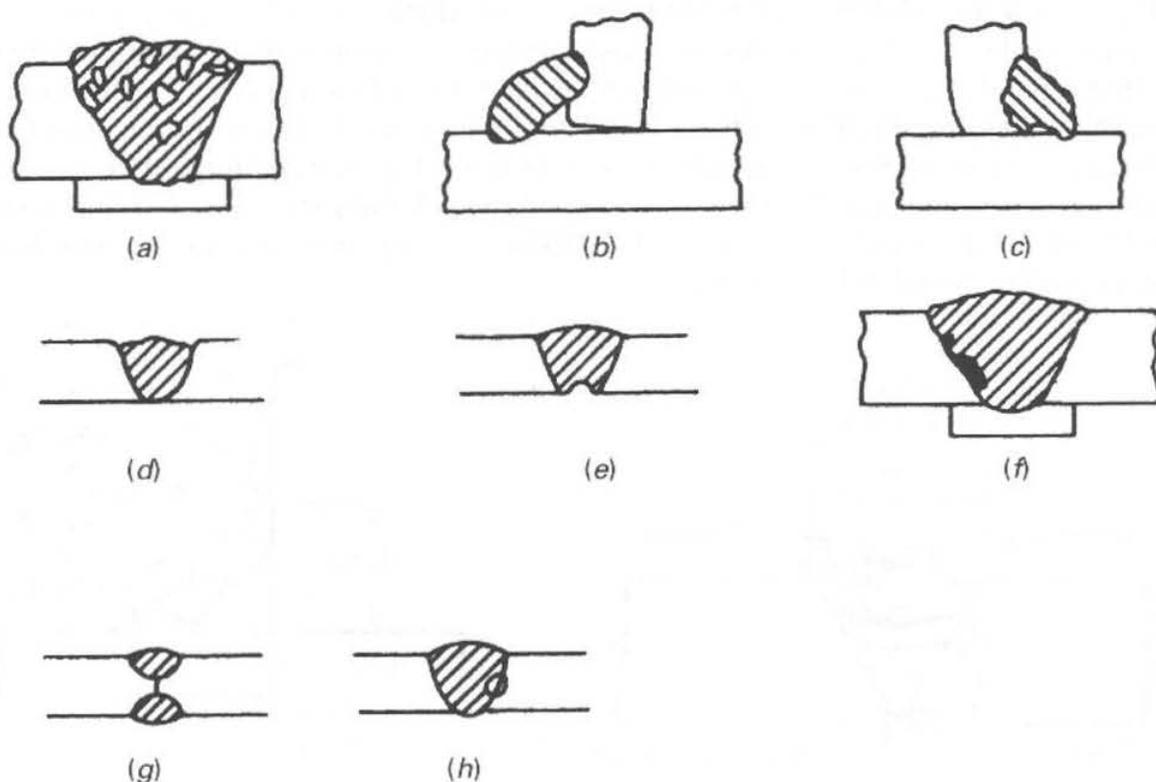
Algunos defectos de soldadura: (a) porosidad; (b) penetración inadecuada; (c) fusión incompleta; (d) soldadura incompleta; (e) cavidad en raíz; (f) inclusión de escorias; (g) penetración incompleta de la raíz; (h) función lateral incompleta.
